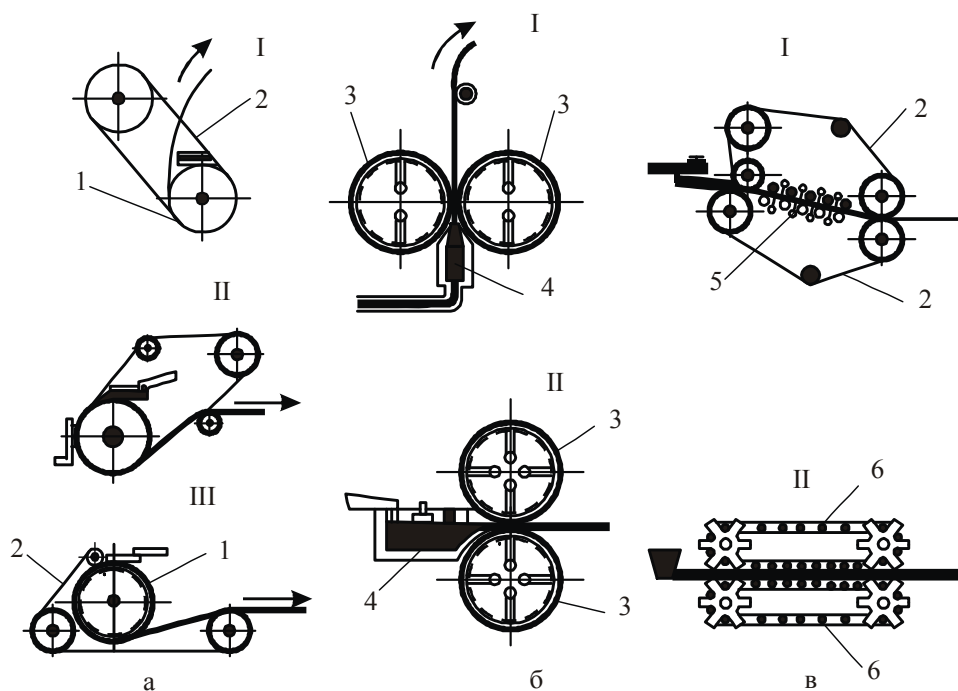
Типи установок безперервного розливу металу в рухомі кристалізатори: а) – роторні: I – Проперці; II – Рігомонті; III – RSC; б) – валкові: I – Хантер-інжинірінг; II – Лешіне; в) – стрічкові: I – Хазерлент; II – Хантер-Дуглас; 1 – жолобчатий обір; 2 – стрічка; 3 – порожнисті валки; 4 – роздільча коробка; 5 – пластинчастий ланцюг; 6 – роликовий ланцюг.
